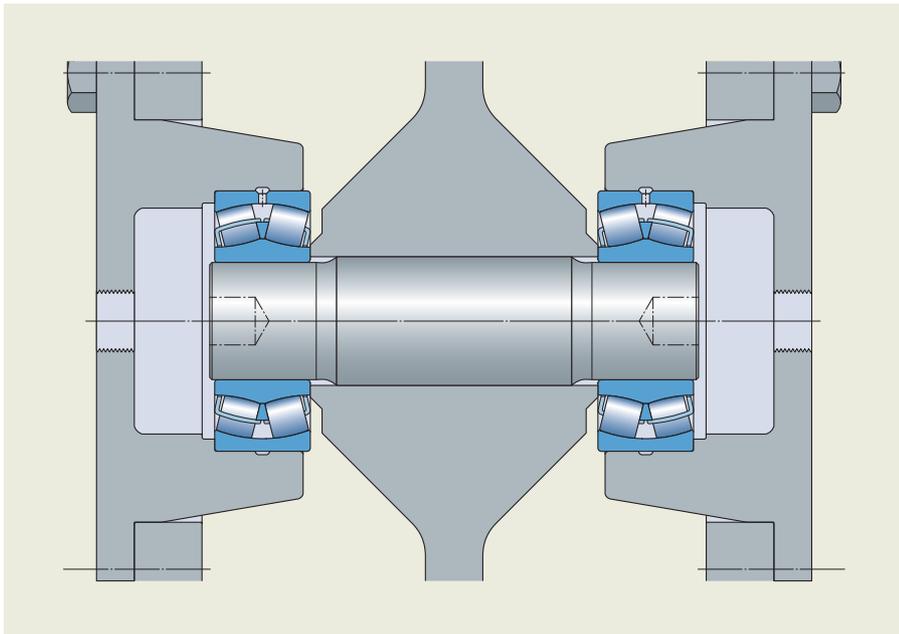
Disposición de rodamientos típica para engranajes intermedios de la sección de secado
